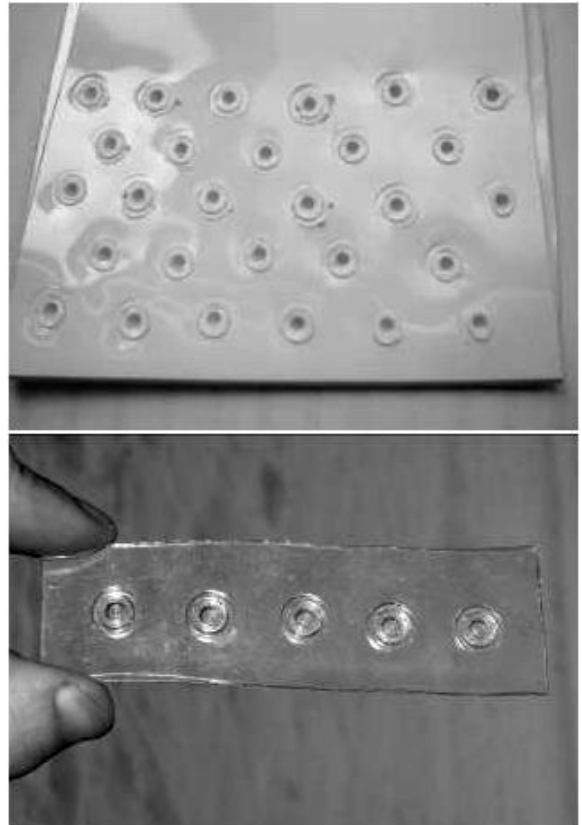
Сварные швы лент из полипропилена и ПВХ.
